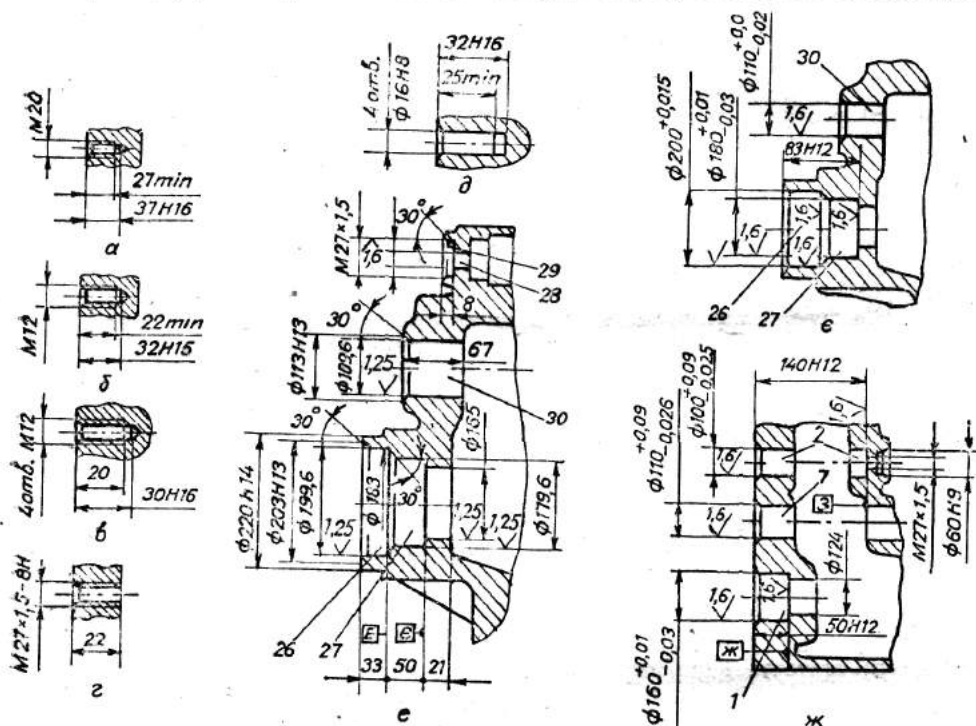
Схеми обробки елементів корпусу редуктора:
